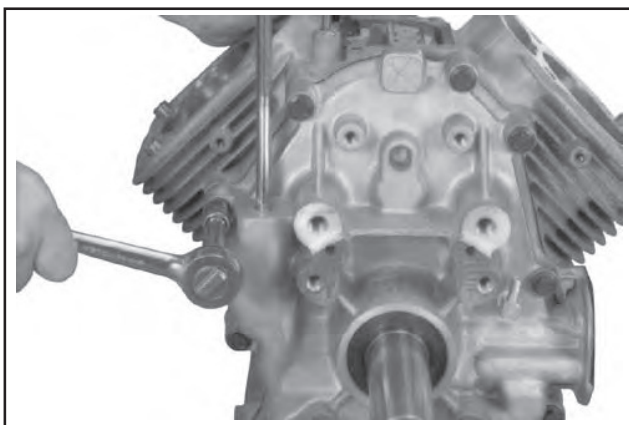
Entfernung der zehn Anschlüsse Verschlussplatte.
